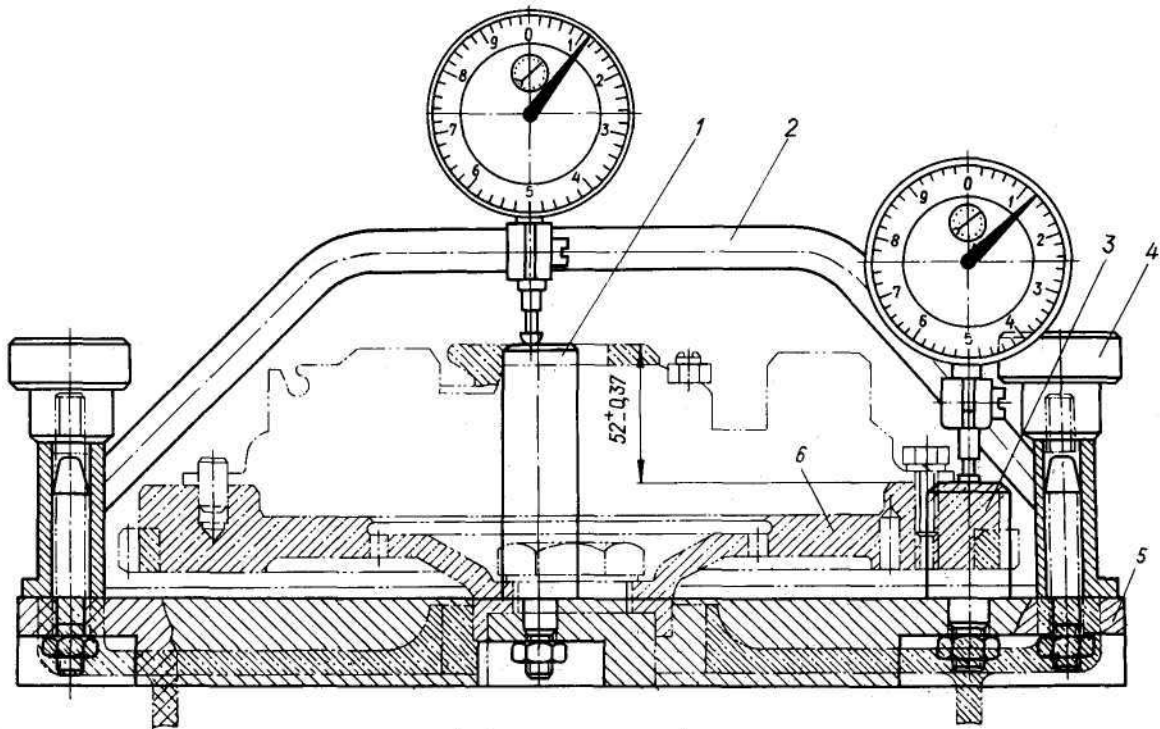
Приспособление для проверки биения торца маховика и для регулировки положения пяты рычагов сцепления:
